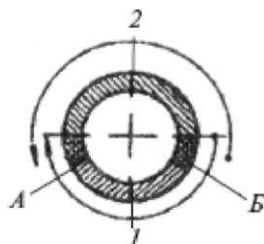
Последовательность сварки неповоротного стыка труб диаметром до 150 мм
